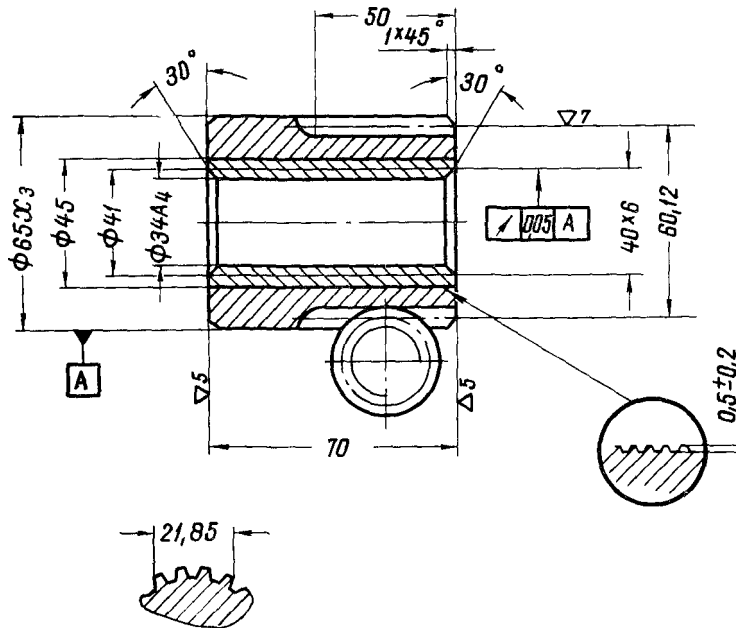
Гайка биметаллическая. Деталь 6М82-7-101
